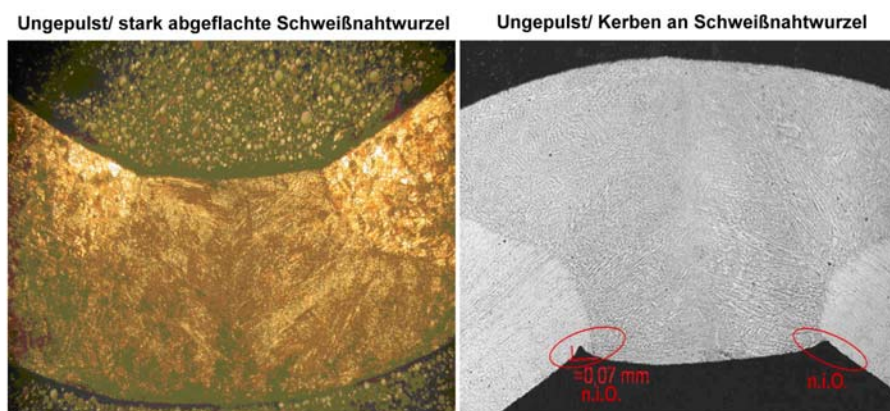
Schweißnahtgeometrie mittels WIG-Gleichstrom geschweißter Rohre
